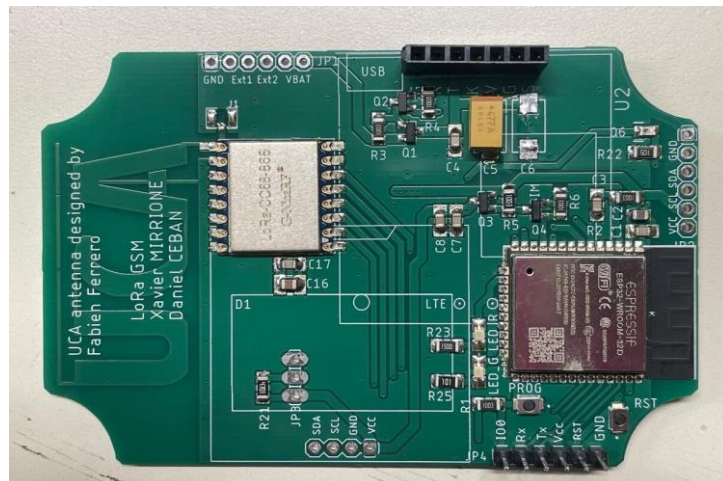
Carte PCB intégralement équipée, vue de dessus.
